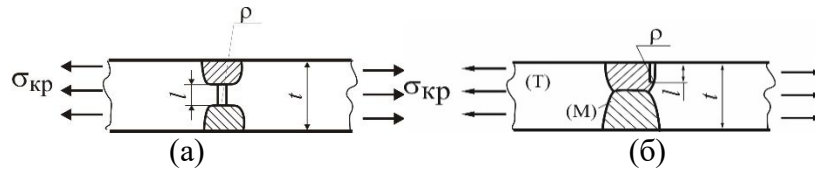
Фрагмент сварного соединения с внутренним непроваром (а) и поверхностным несплавлением на границе сплавления (б):
